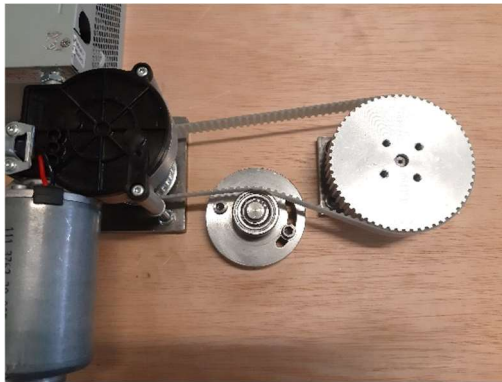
Conjunt tensor instal·lat a la transmissió per corretja dentada.
